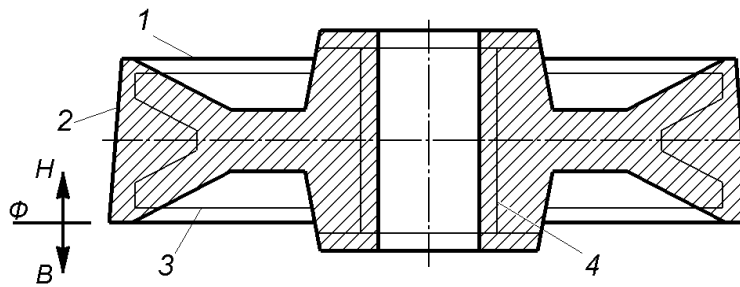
Виливок шків з сірого чавуну, виготовлений у піщано-глинистій формі
